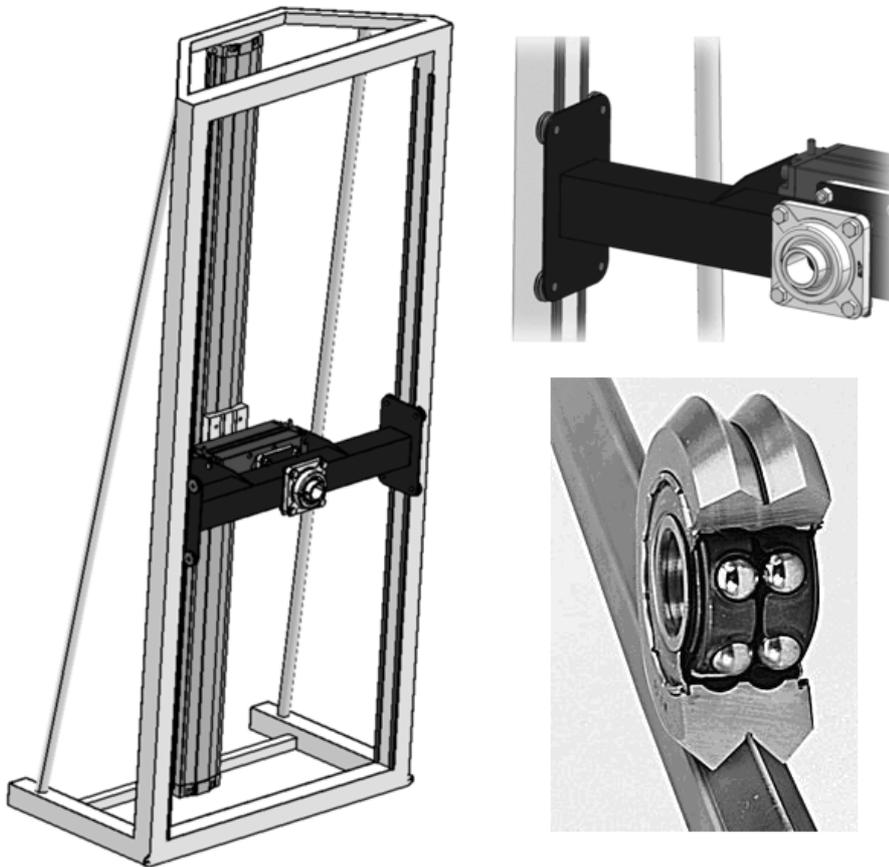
Châssis de la machine, illustration du mécanisme de translation vertical
